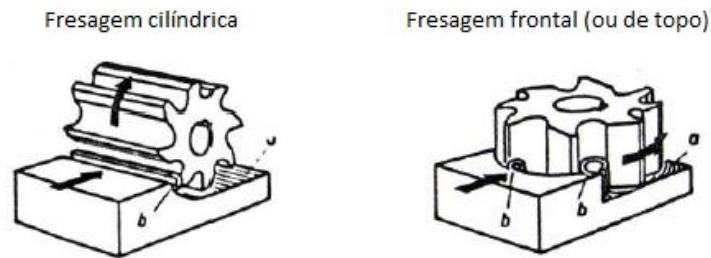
Fresagem cilíndrica e fresagem frontal, adaptado de [23].
